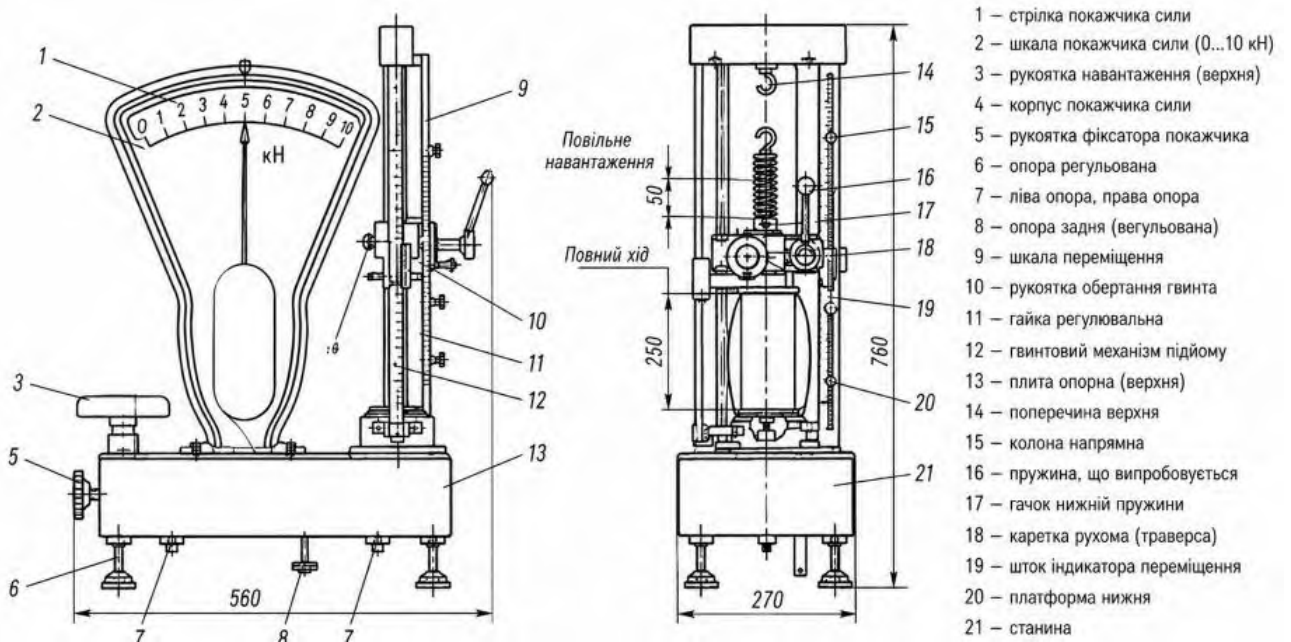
Схема конструкції установки МИП-0,01 5053
